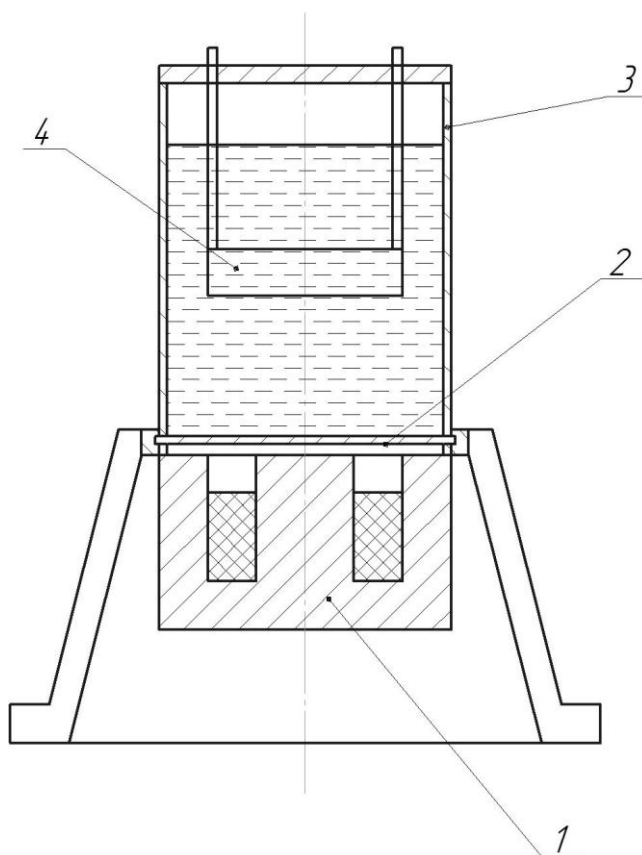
Эскизный проект предлагаемой конструкции мойки
